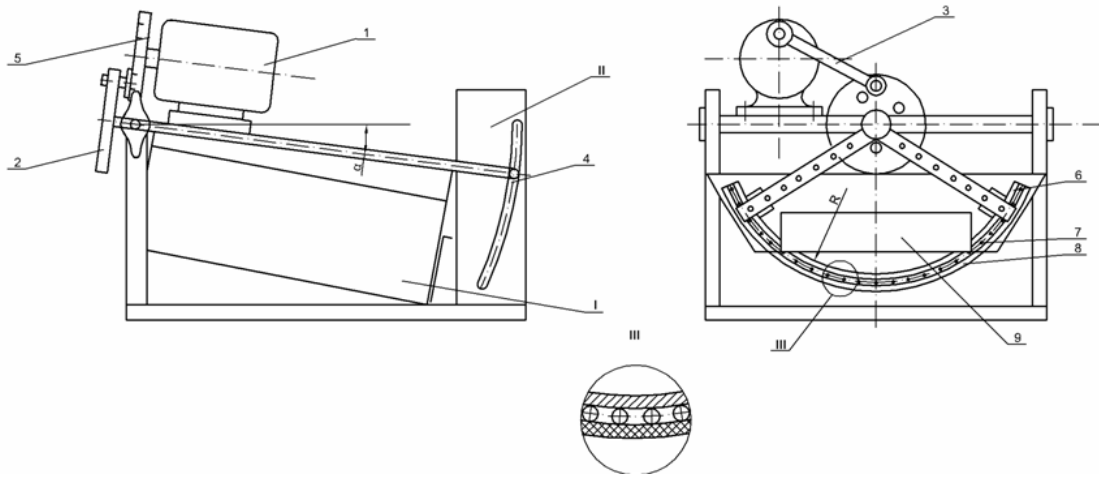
Схема конструкції засобу формування гранул ОМД: 1 – електродвигун; 2 – приводний шків; 3 – шатун; 4 – пристрій регулювання кута нахилу камери обкочування; 5 – ведучий шків; 6 – робоча поверхня камери обкочування; 7 – нагрівальний елемент камери обкочування; 8 – ізоляційний елемент камери обкочування; 9 – заслінка; I – камера обкочування; II – рама (межі регулювання: $\alpha = 5...25^\circ$, $R = 0,5...1,5$ м, $i_{\text{нагр.}}^{\text{поверх}} = 60...120^\circ$).
